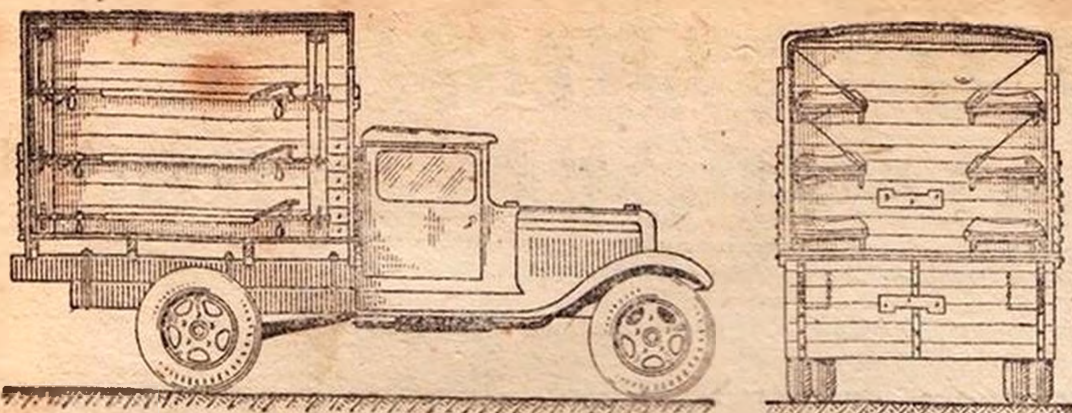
Автомобиль ГАЗ-АА, приспособленный для перевозки раненых.
